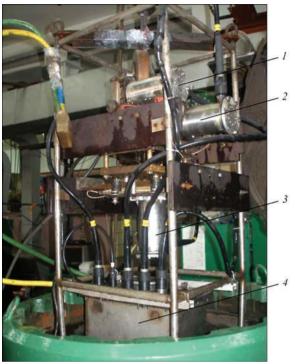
Автомат для сварки-наплавки под водой с электродвигателями механизмов: 1 — продольного; 2 — поперечного перемещения; 3 — подачи электродной проволоки; 4 — блок управления погружной
